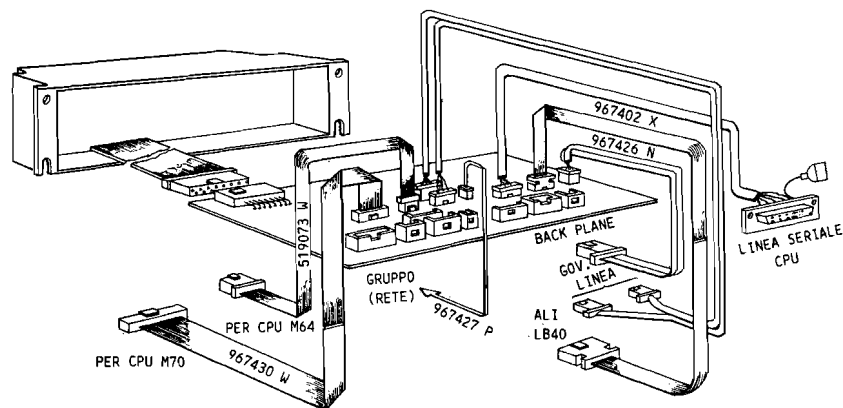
Vista posteriore della console estesa e della piastra REDAC
